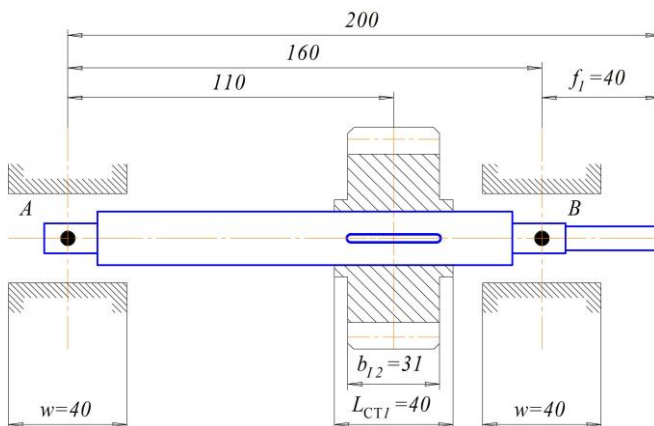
К компоновке быстроходного вала цилиндрического двухступенчатого редуктора
